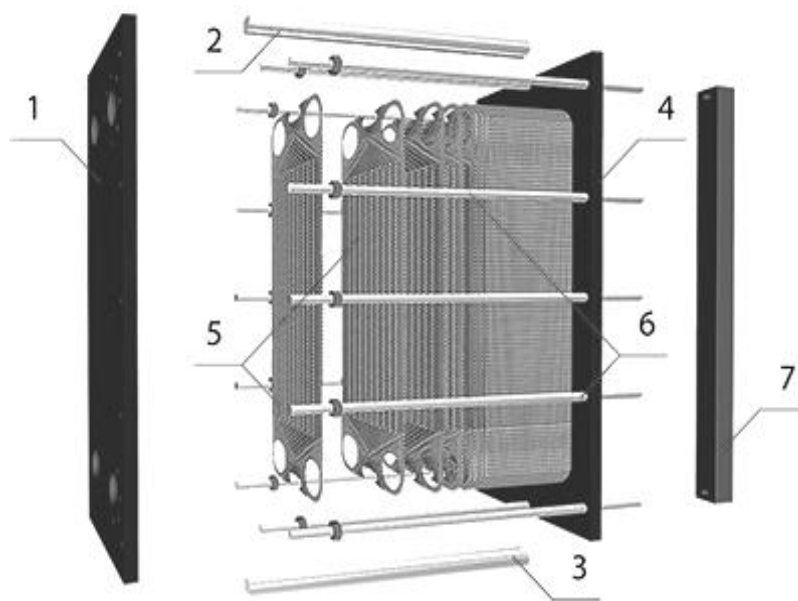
Устройство разборного пластинчатого теплообменника: 1 - неподвижная плита с соединительными патрубками; 2 - верхняя направляющая; 3 - нижняя направляющая; 4 - задняя прижимная плита; 5 - теплообменные пластины с уплотнительными прокладками; 6 - комплект резьбовых шпилек; 7 - задняя стойка.
